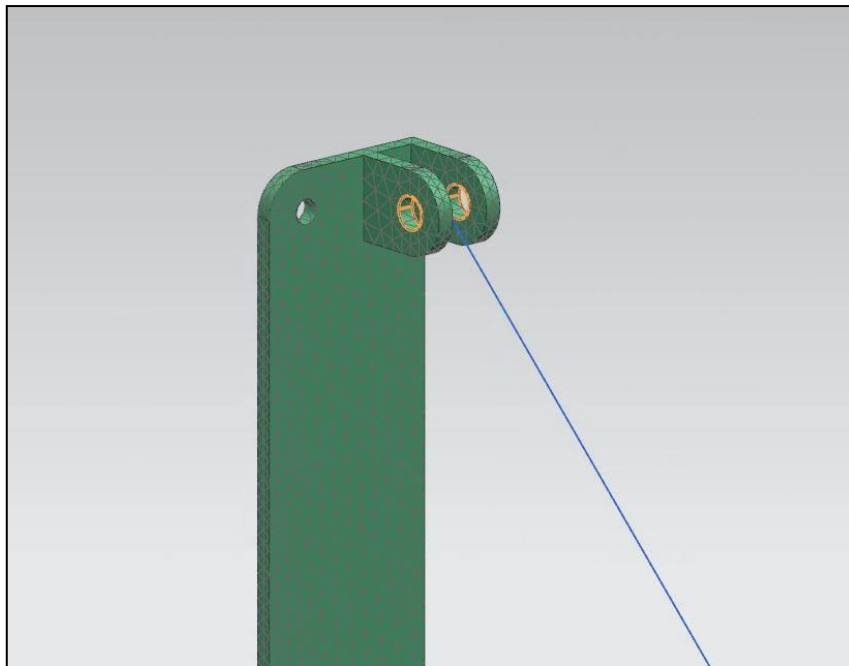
; Befestigungsflächen (gelb) der blockierten Gasdruckfeder
